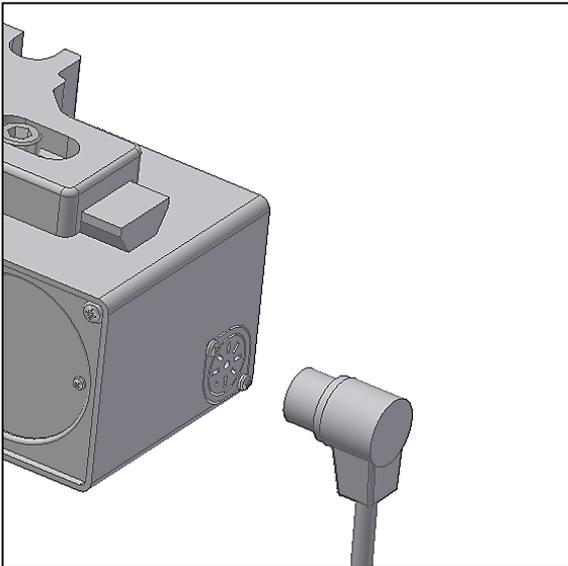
Verbinden Sie die Kabel beider Motoren.
